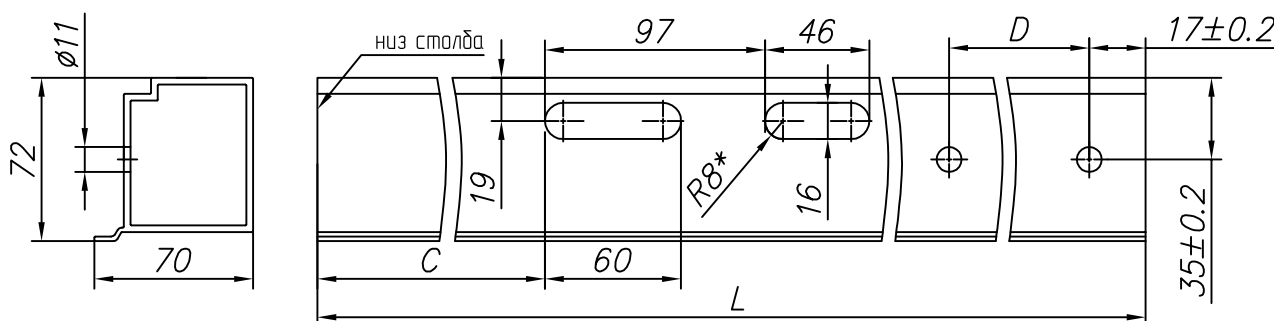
Изготовление столба притвора с пазом для ответной пластины замка для калитки с правым открыванием
